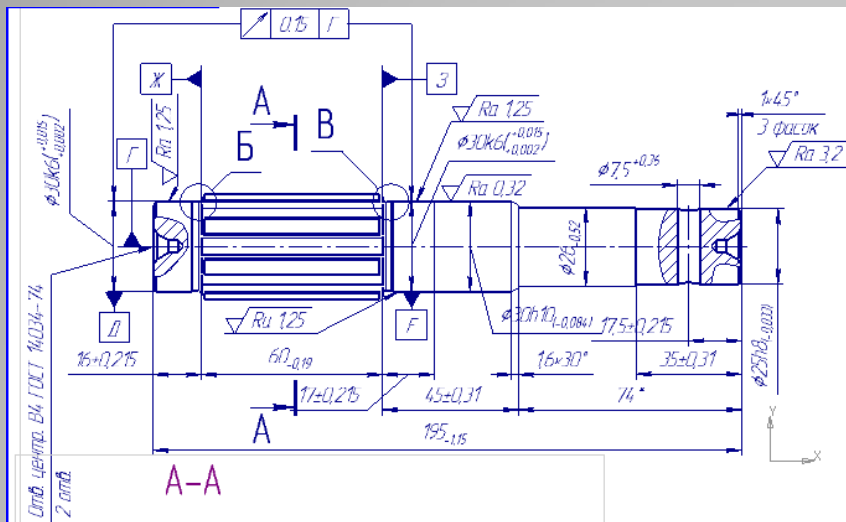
Робоче креслення валу коробки відбору потужності
